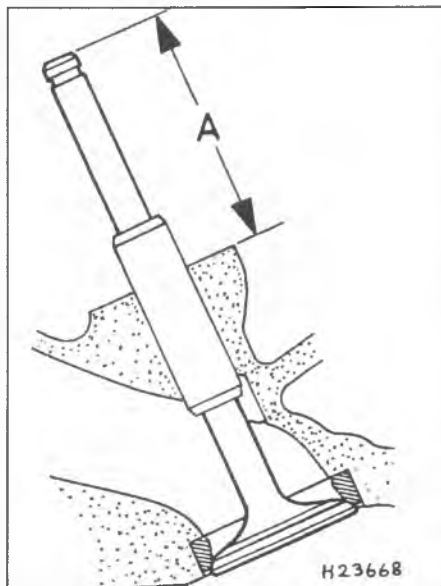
в. Измерение установочной высоты стержня клапана (А) – бензиновый двигатель
